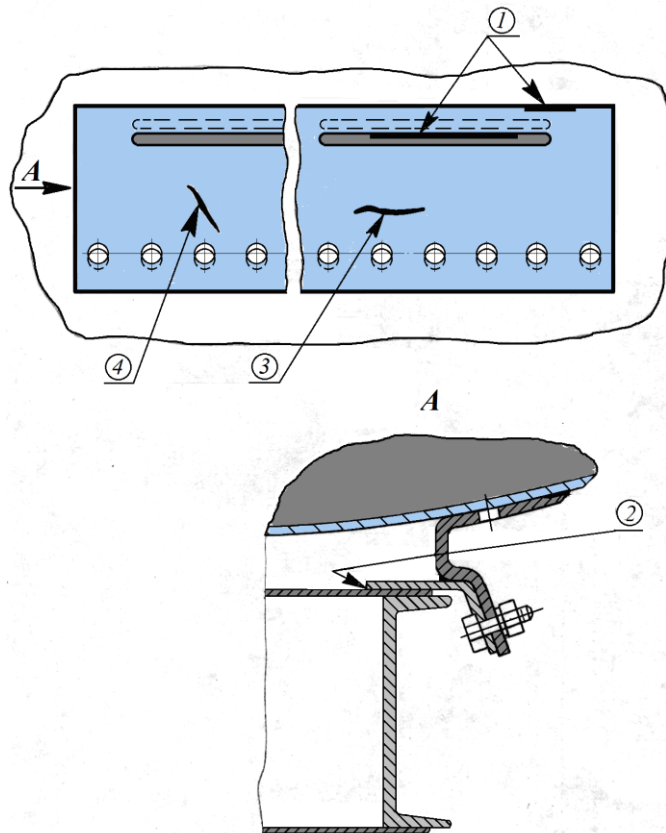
Вузол кріплення котла до хребтової балки
